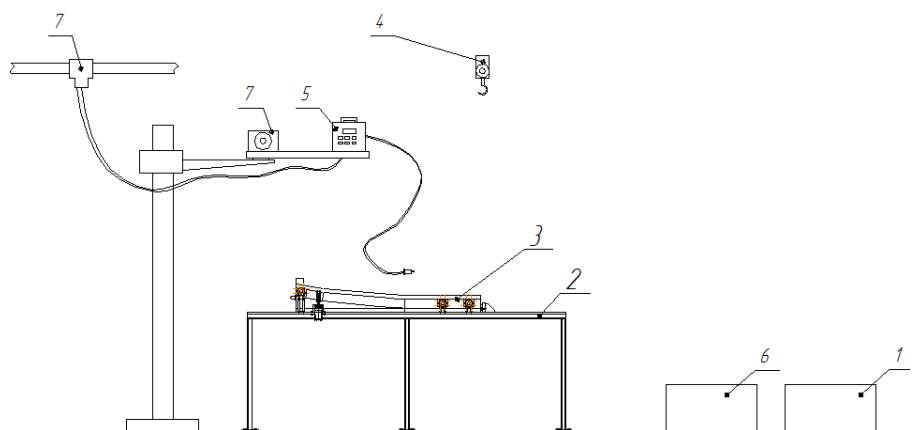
Схема компоновки рабочего места общей сборки-сварки:
